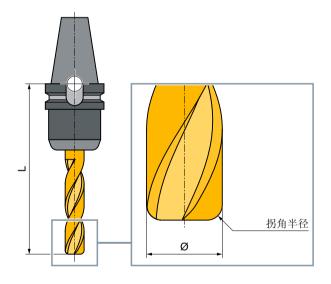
3D 刀具,例如:带倒圆的立铣刀(121型)
